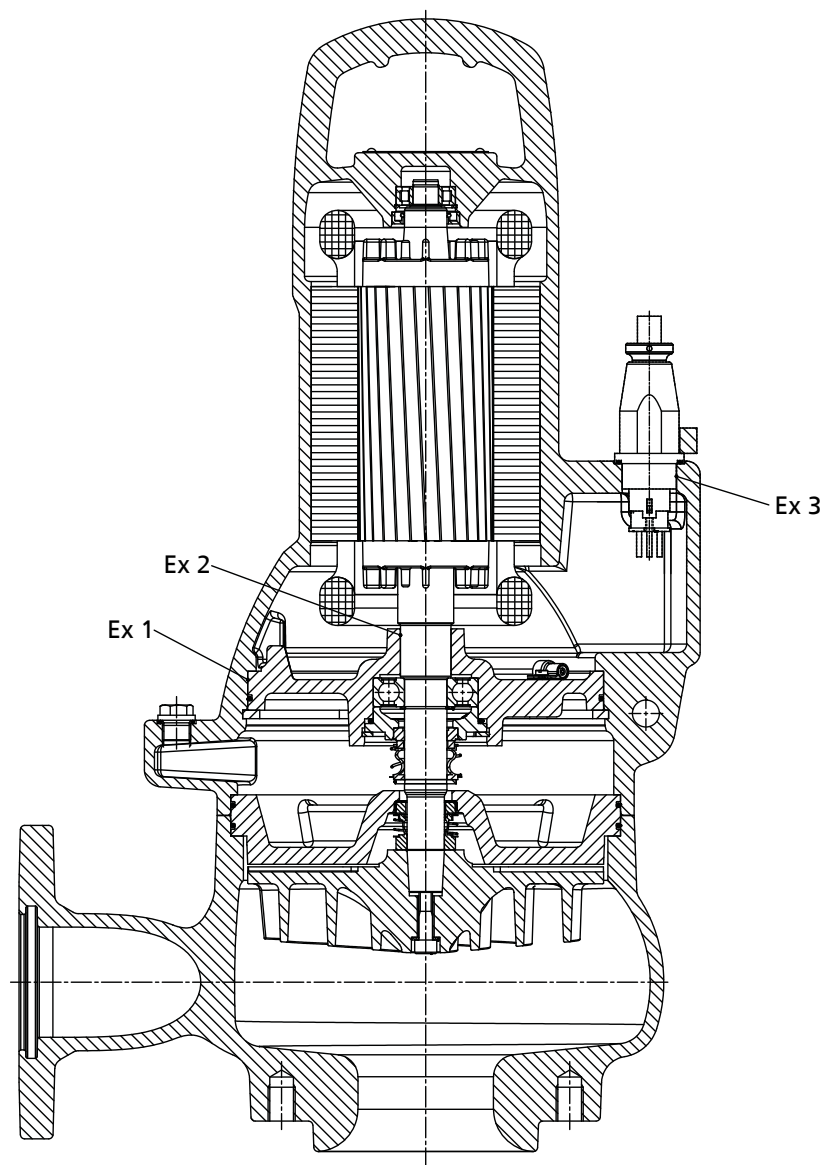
Поверхности взрывозащитных зазоров Amarex KRT, тип двигателя 1
